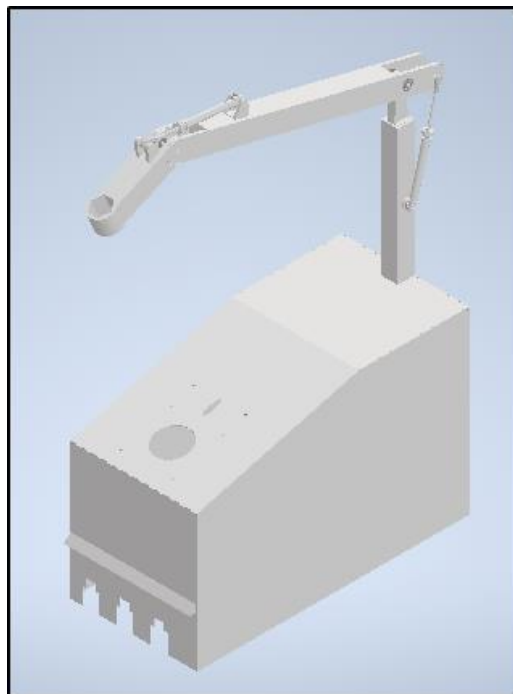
Ensamblaje Desmontadora de Ruedas
